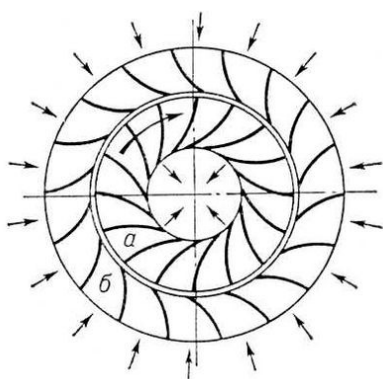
Схема реактивной гидротурбины: а — рабочее колесо; б — направляющий аппарат.
